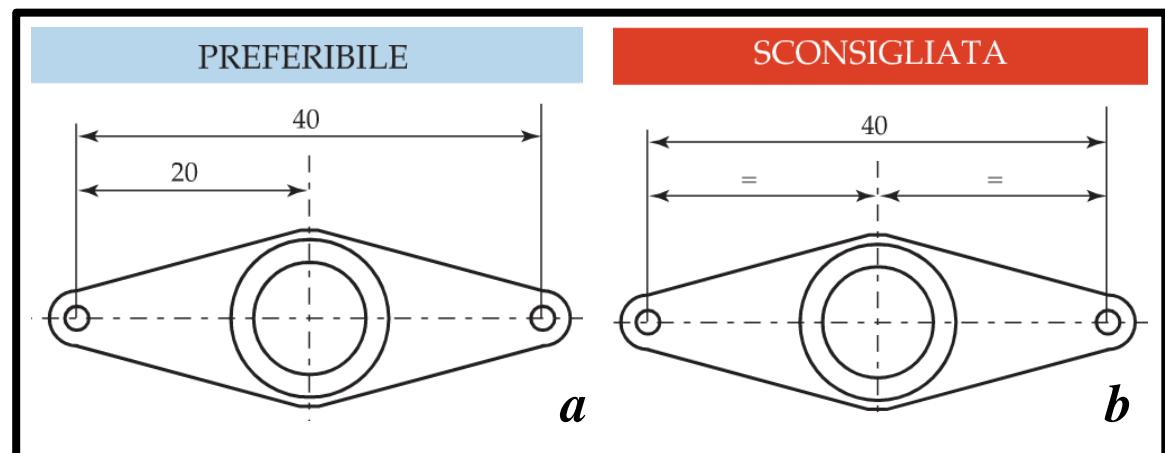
b) Indicazione obsoleta che il centro dei due fori è simmetrico rispetto all'asse di simmetria
